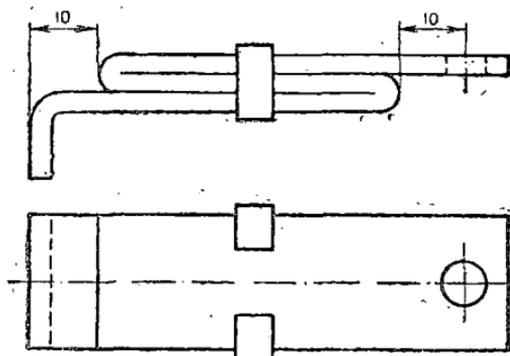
Нагревательный элемент из полосы (с дополнительным изгибом)
